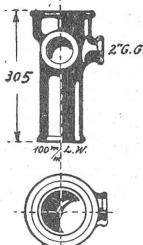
mit zwei 2" Gewindeanschlüssen
